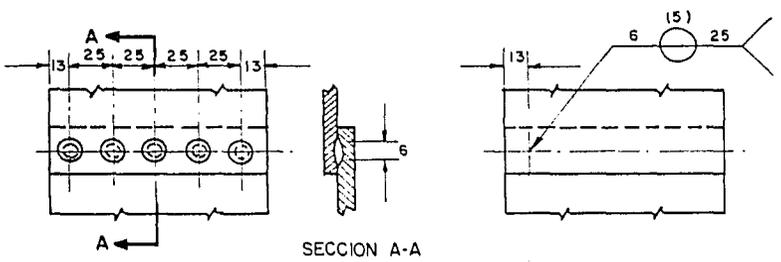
APLICACION DE DIMENSIONES PARA SIMBOLOS DE SOLDADURA DE FUSION
